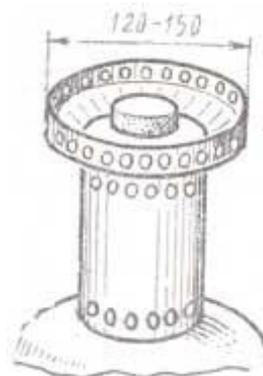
Самодельный кожух-отражатель — подставка для варочной посуды (к примусу «Шмель»)
